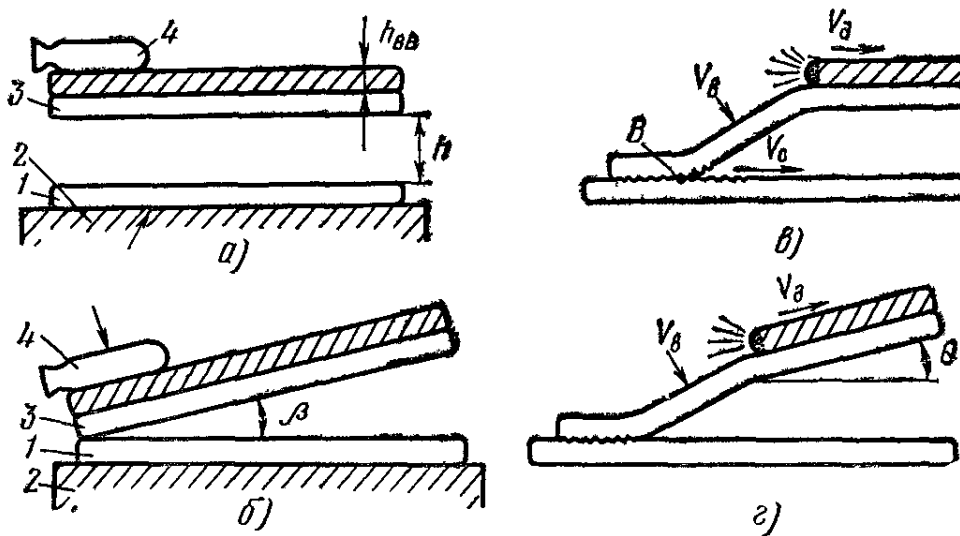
Принципиальные схемы сварки взрывом
